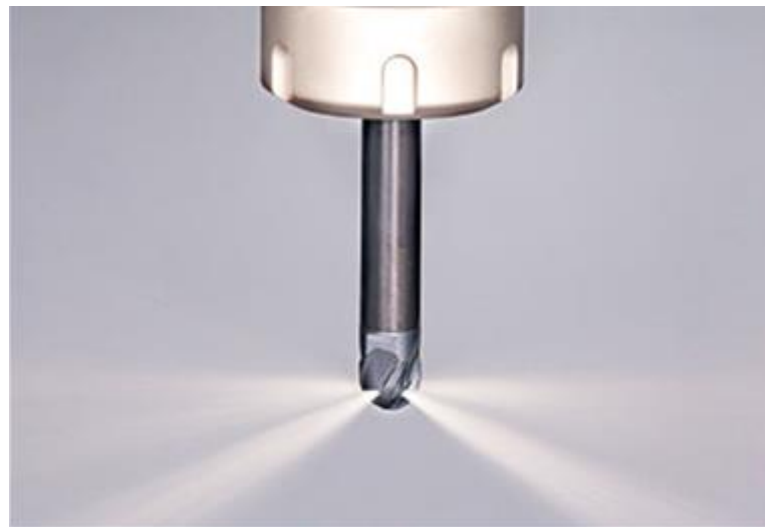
Схема подачі ЗОР через сопла інструмента.
